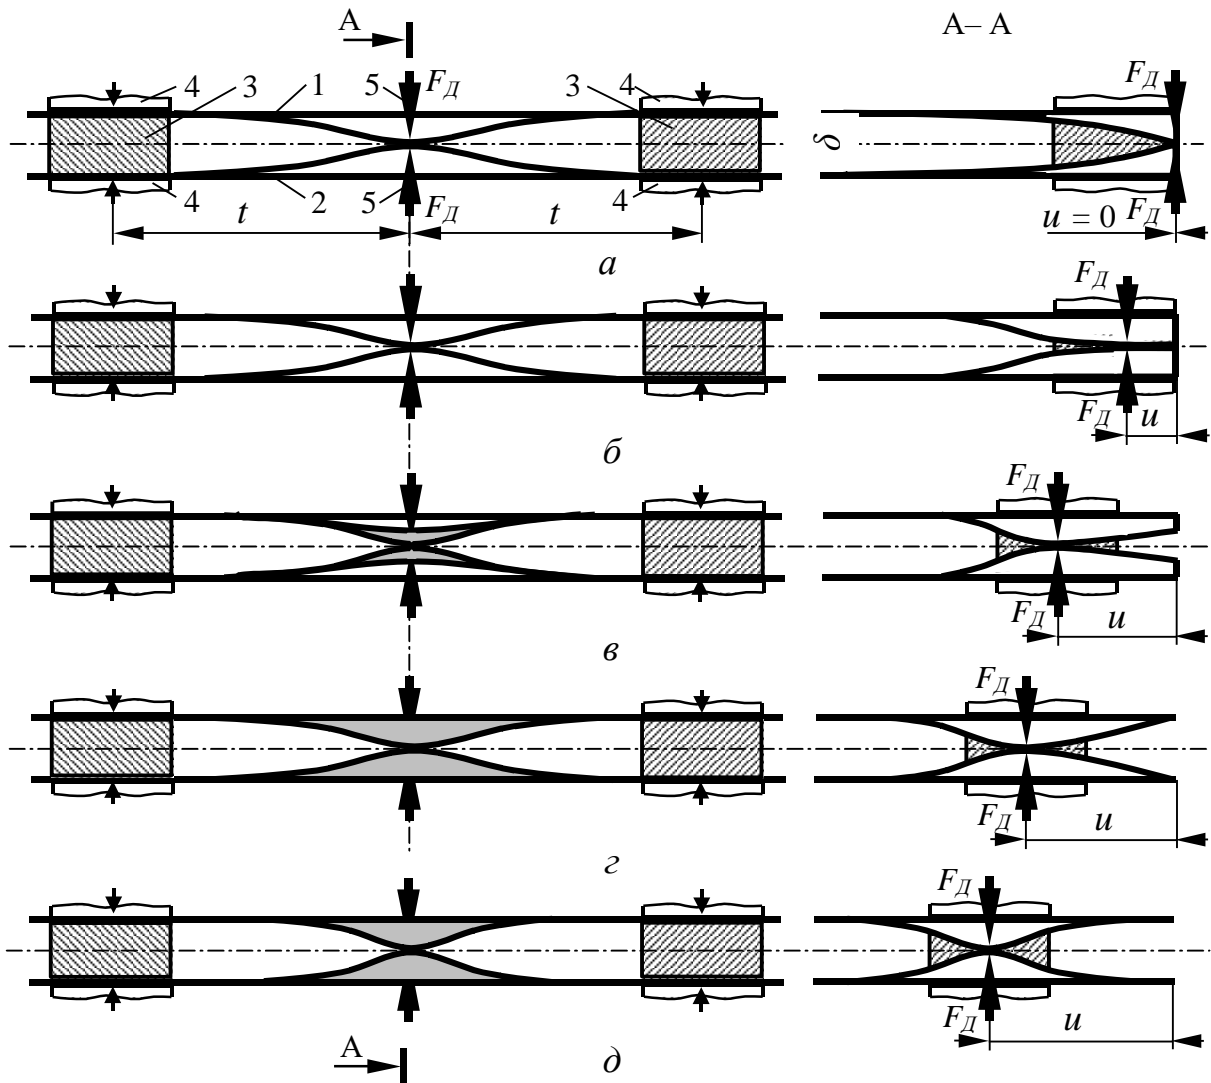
Схема деформації зварювальних деталей: 1, 2 – деталі;
